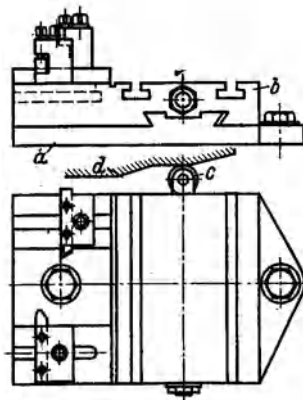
Werkzeugschlitten mit Querbewegung und Kopiereinrichtung auf dem Revolverschlitten. Das Unterteil *a* wird auf einem der Werkzeugschlitten befestigt. Der Oberschlitten *b* besitzt mehrere T-Nuten zum Befestigen von Stahlhaltern. Eine Leitrolle *c*, die auch durch einen Taststein ersetzt werden kann, ist durch Spindel verstellbar mit dem Oberschlitten *b* verbunden. Auf den Ecken des Revolverkopfes, der nicht an der Längsbewegung teilnimmt, wird durch einen Halter eine passend ausgearbeitete Kopierschiene *d* befestigt, an welcher die Leitrolle entlang gleitet und dem Oberschieber die notwendige Planbewegung erteilt.
